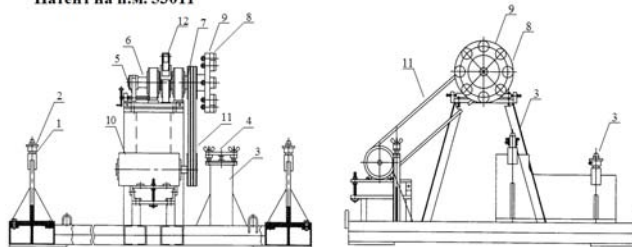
Установка для распрессовки-запрессовки конических соединений
